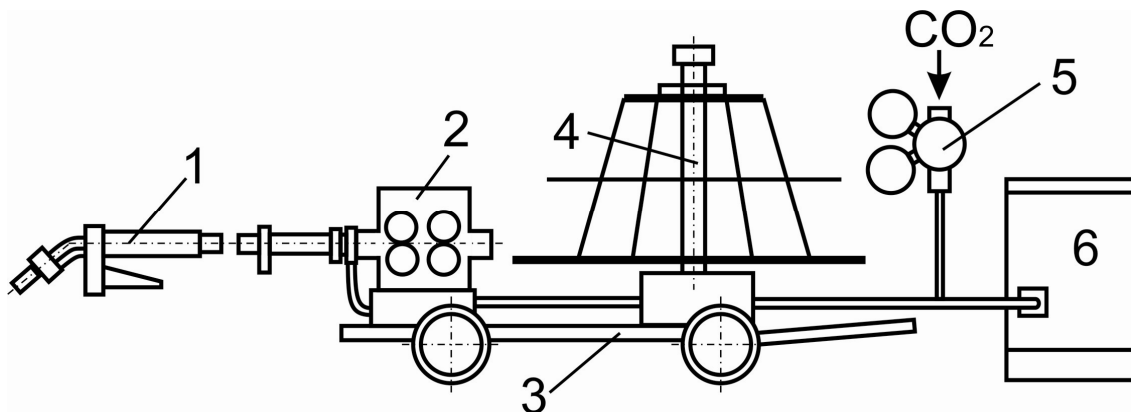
Схема полуавтомата А-1197: 1 – держатель (газоэлектрическая горелка), 2 – механизм подачи, 3 – тележка, 4 – катушка с бухтой сварочной проволоки, 5 – редуктор, 6 – шкаф управления.
